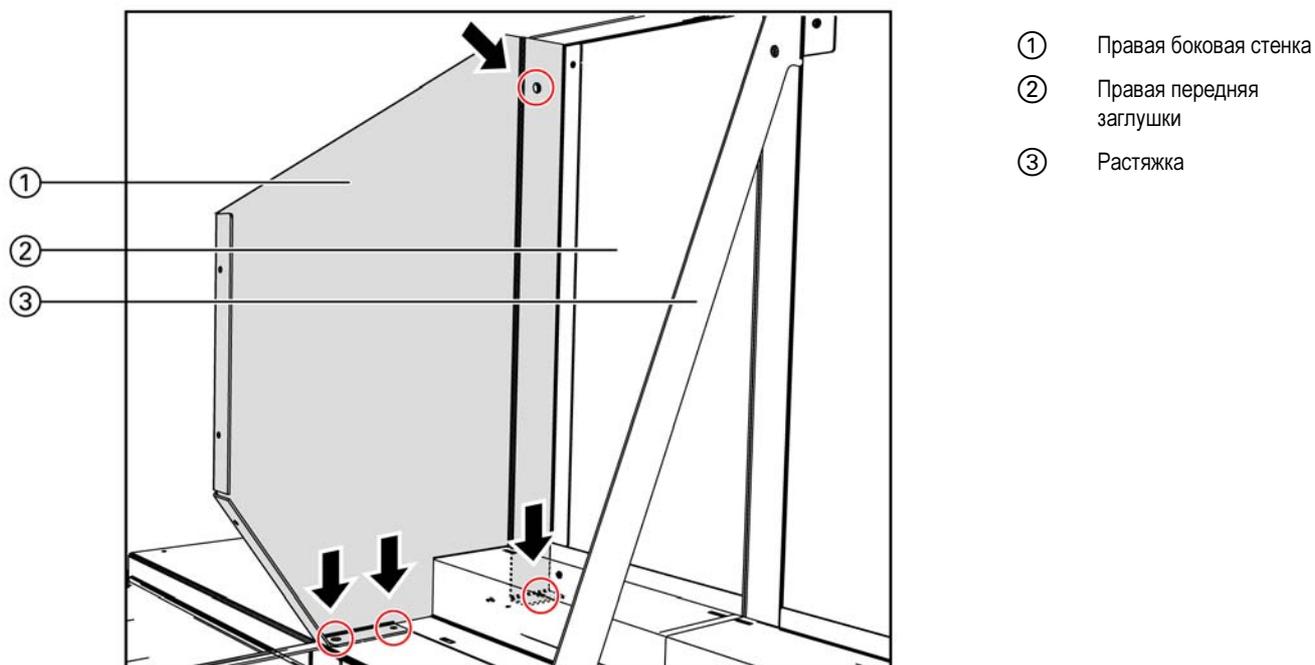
Точки крепления боковой стенки надстройки абсорбера к емкости установки и передней заглушке (вид сзади на правую сторону установки)
